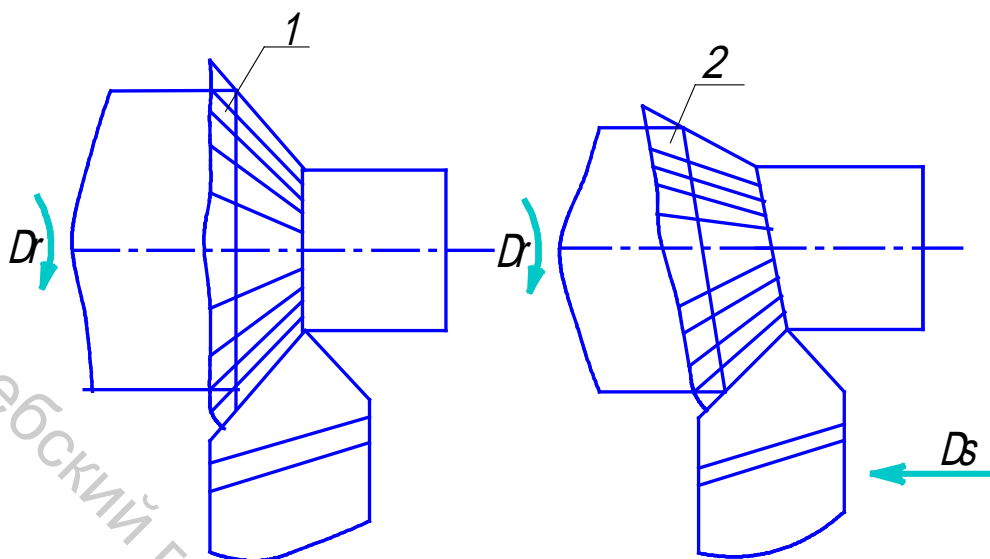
Поверхность резания и поверхность главного движения:
